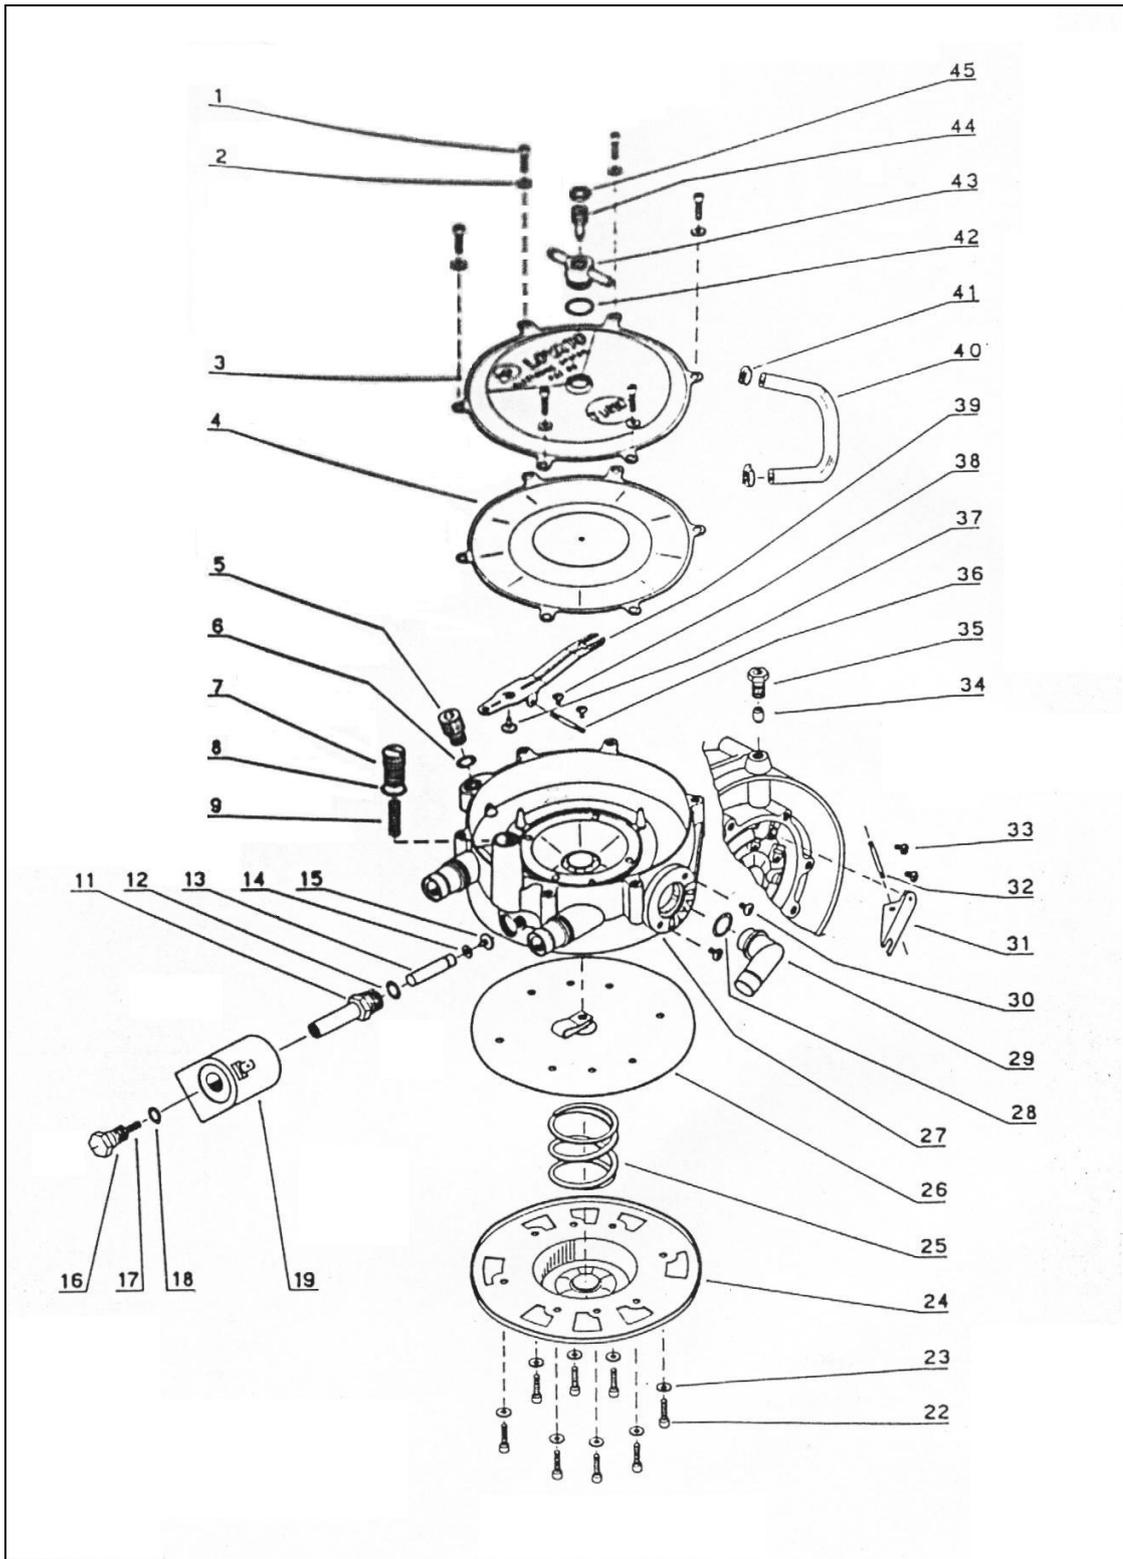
Esquema del despiece del Reductor-Vaporizador GLP Turbo Electrónico
